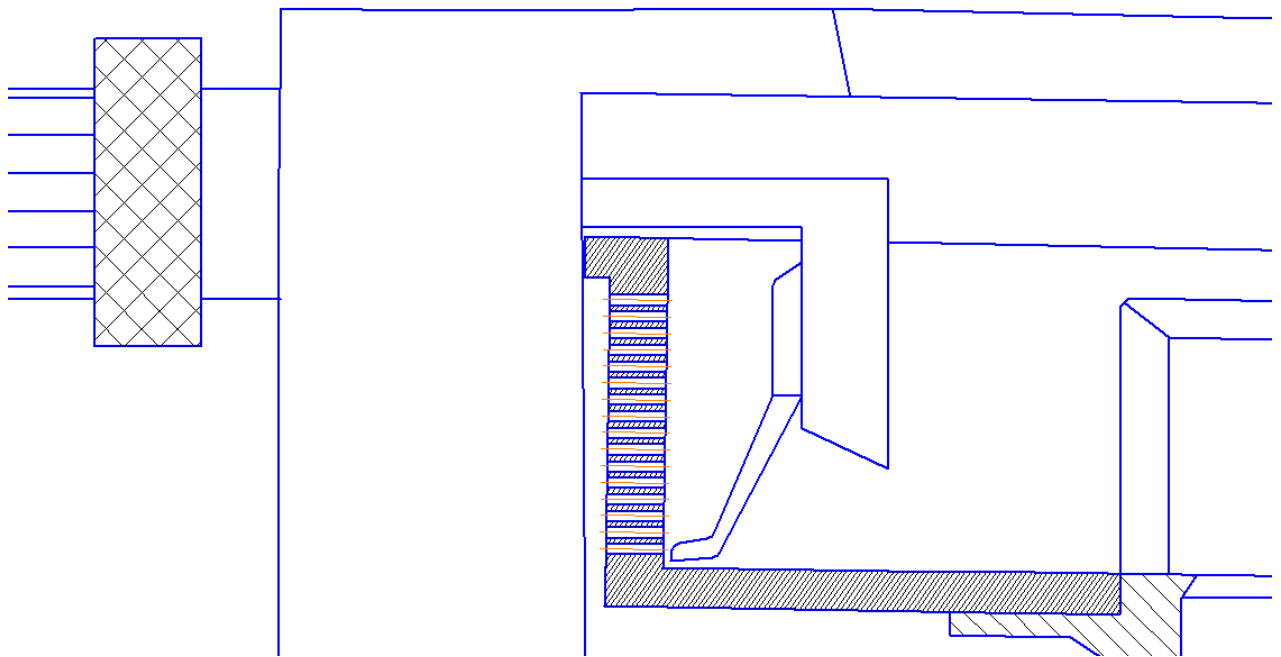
Розташування запропонованого скребка на нерухомому ножі.
